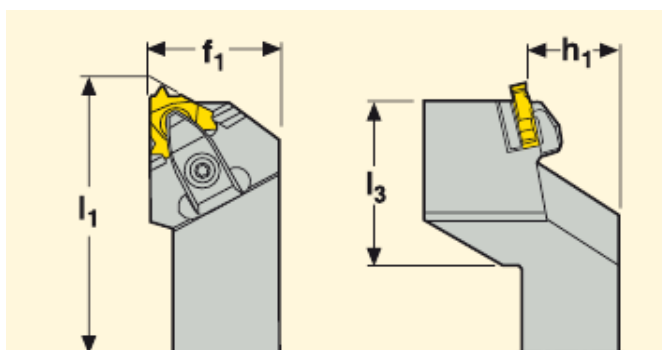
Механічне кріплення твердосплавної пластини для виготовлення різьби
